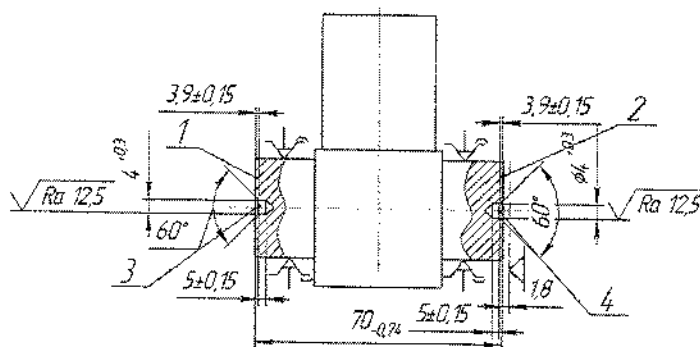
Фрезерно-центровальная операция с ЧПУ
